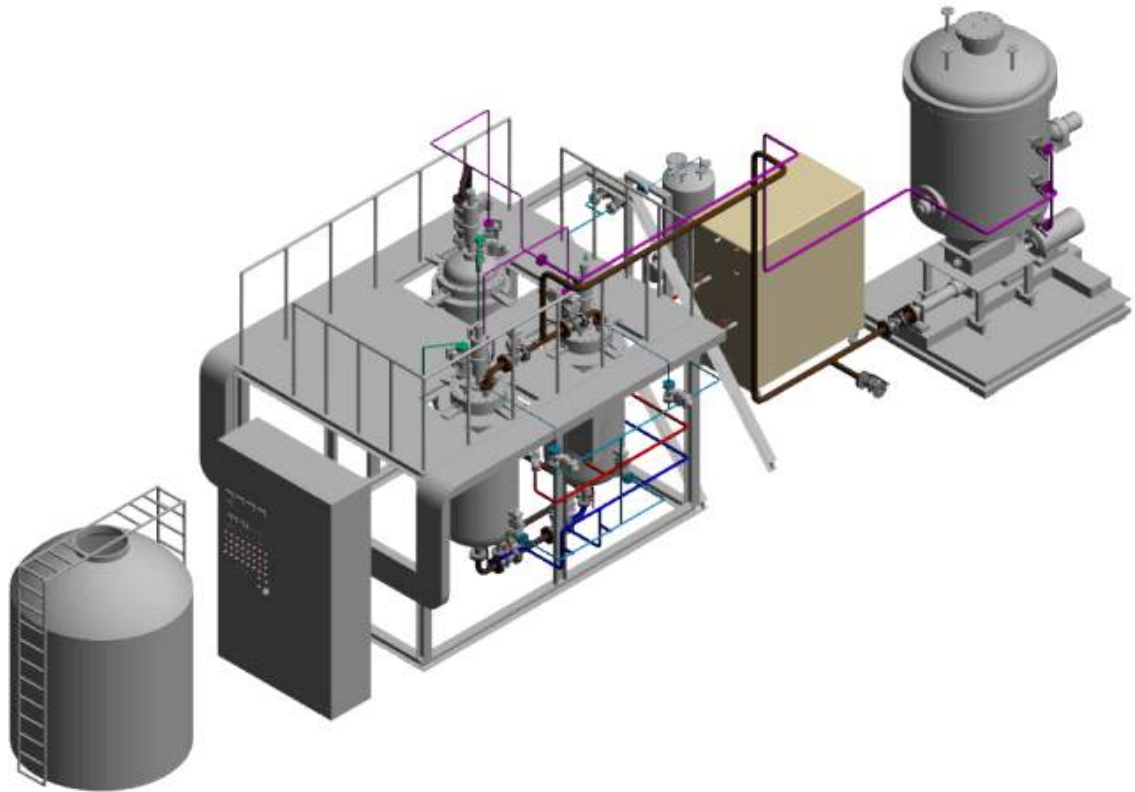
Pilot plant급 수열탄화 시스템 3D 설계도
